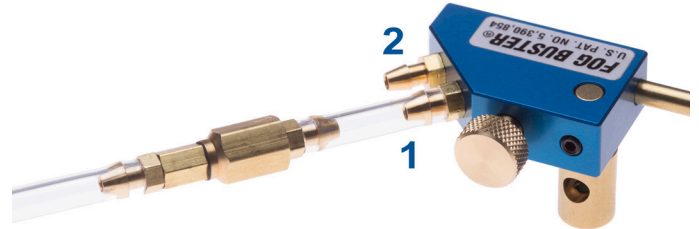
Anschluss 1 für Kühlschmiermittel, 2 für Druckluft
